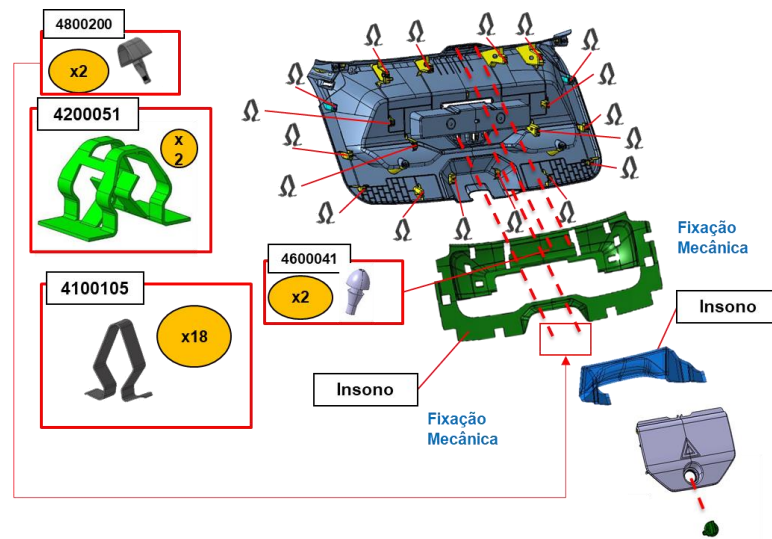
Peça produzida pelo molde 9298 com os componentes
